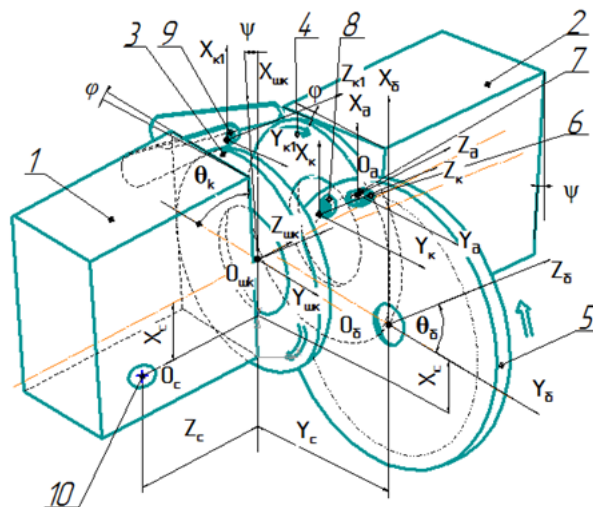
Розрахункова схема формоутворення торців циліндричних деталей з некруглим профілем
